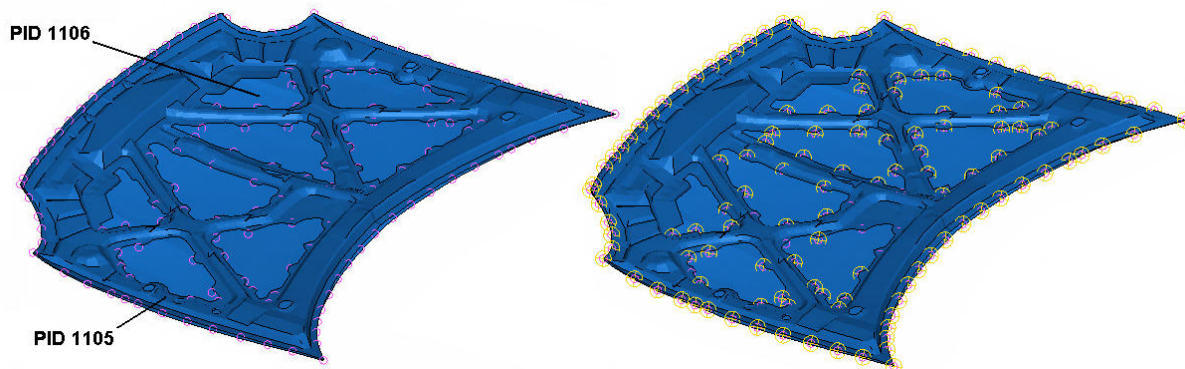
Bodové svary načtené ze souboru [VIP].
